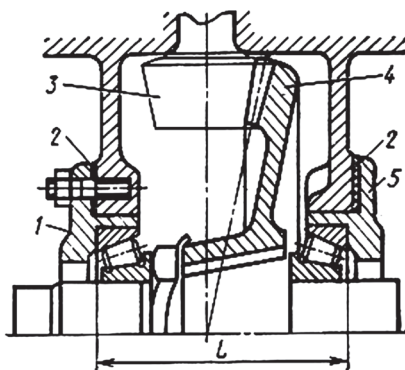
Регулировка осевого положения колес конической передачи и подшипниковых опор
